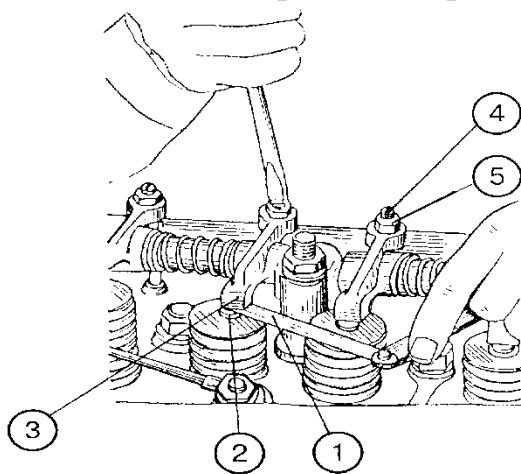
Регулировка зазора между клапанами и коромыслами: 1 – щуп; 2 – стержень клапана; 3 – боек коромысла; 4 – регулировочный винт; 5 – контргайка
